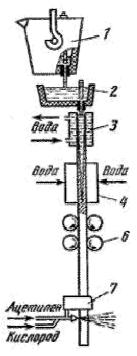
Схема непрерывной разливки стали 1 – ковш; 2 – разливочное устройство; 3 – кристаллизатор; 4 – брызгала; 6 – тяговые ролики; 7 – газовый резак
